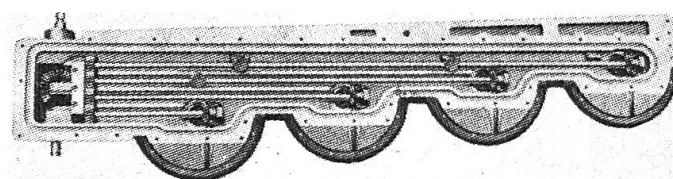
hier für jede Scheibe eine separate Welle mit Kegelnrädern.
